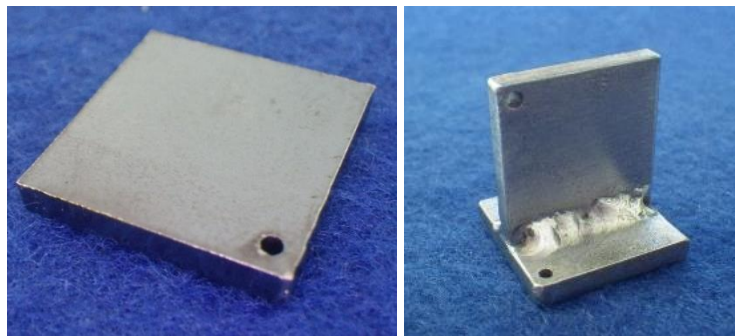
Links: Plättchenprobe, Rechts: Kehlnahtprobe
